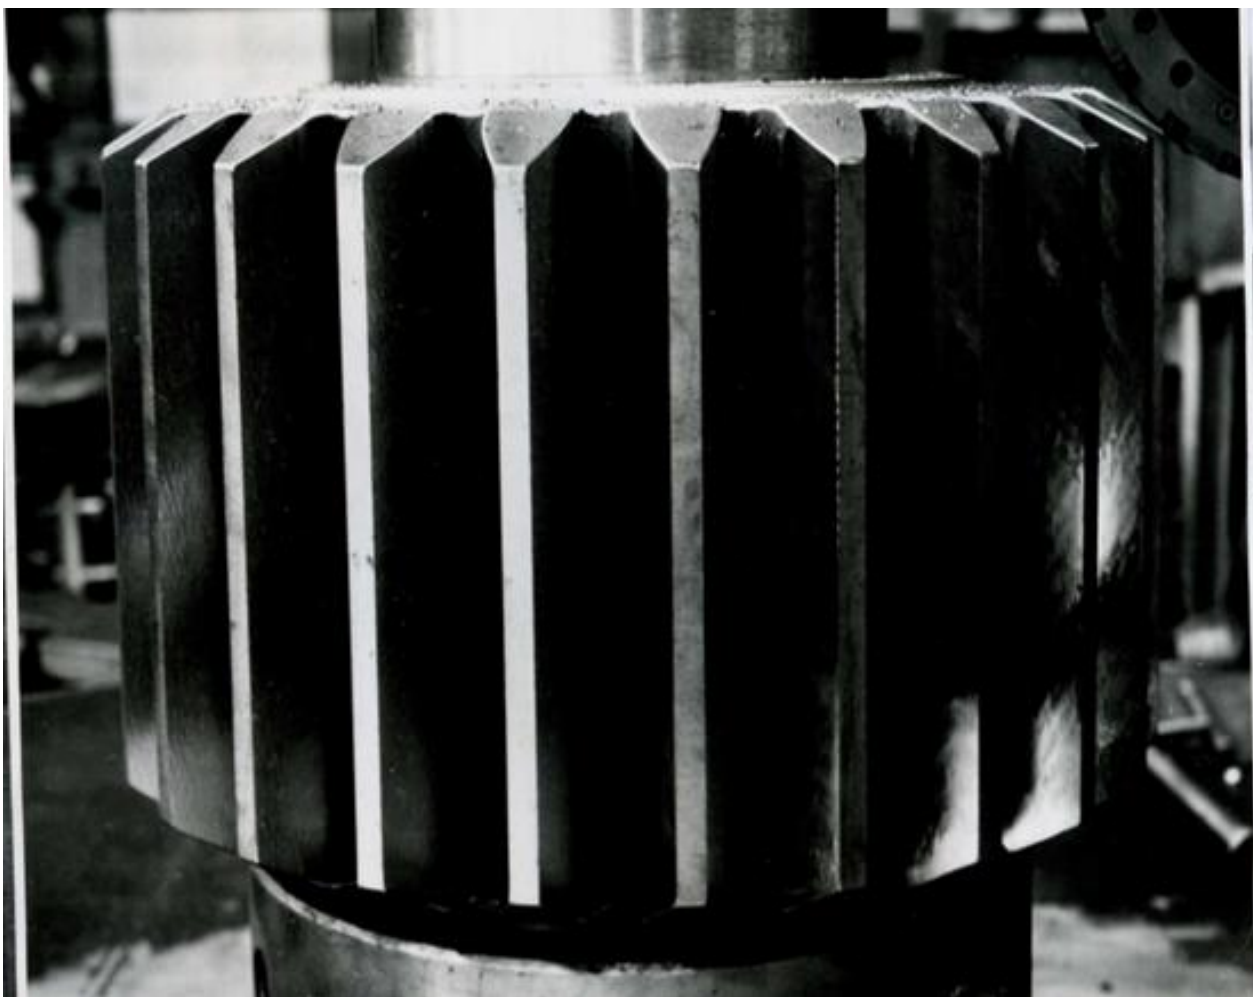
Зубчате колесо $m = 28$ мм, $z_1 = 24$, оброблене за новою лезвійною обробкою після наплавлення зубів
